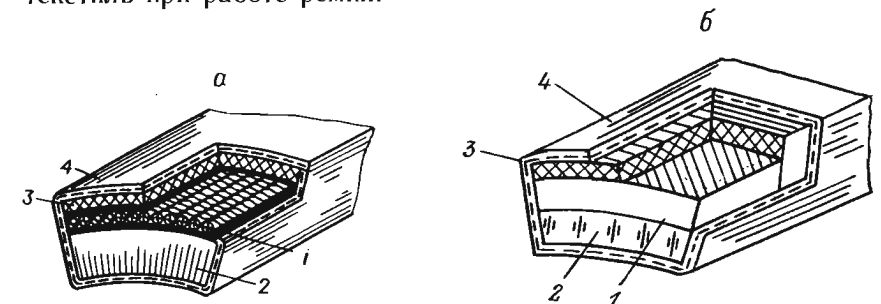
Клиновые ремни кордшнуровой (а) и кордтканевой (б) конструкций: 1 — несущий слой; 2 — слой сжатия; 3 — слой растяжения; 4 — обертка
